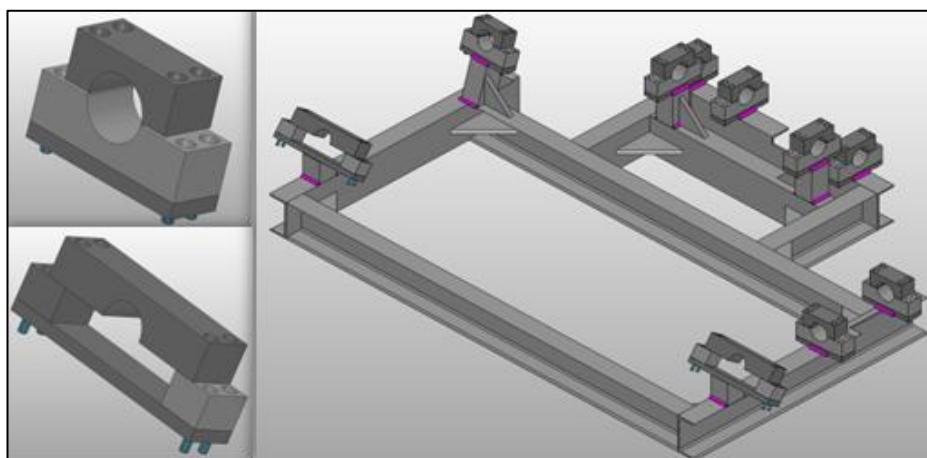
Desain 2D Rangka *Jig welding
